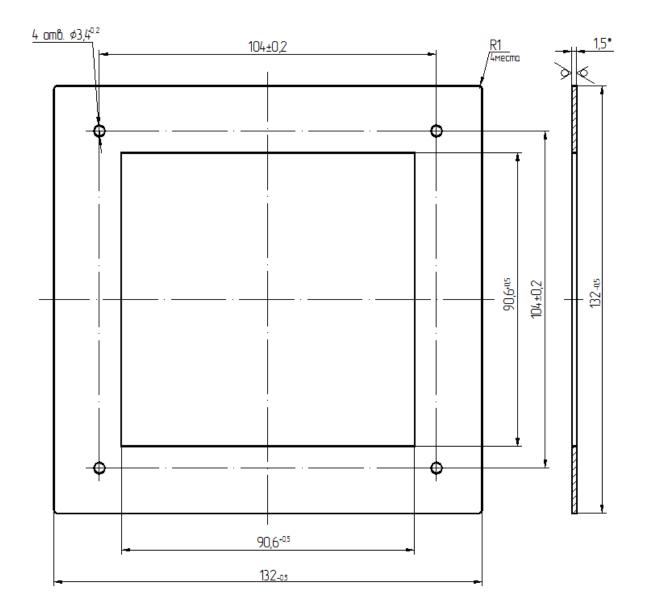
Габаритные и установочные размеры рамки комплекта крепежа устройства
